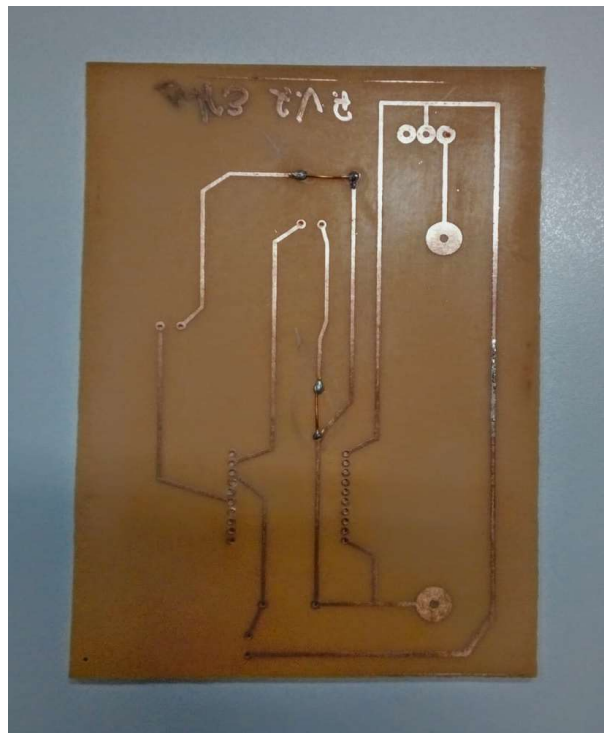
Placa de circuito impresso da base remota. Fonte: autor.
